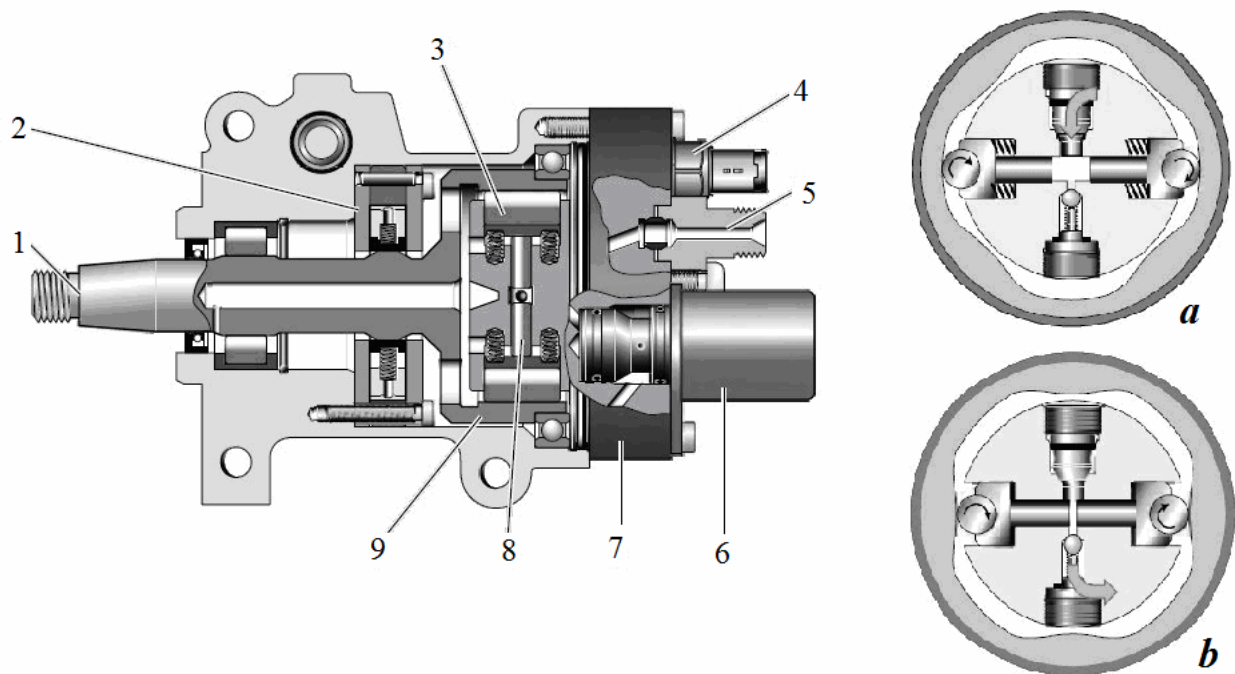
Pompa de injecție DFP 1: a- faza de admisie; b- faza de refulare: 1- ax antrenare; 2- pompa de transfer; 3- rolă; 4- senzor temperatură combustibil; 5- racord de înaltă presiune; 6- regulator de presiune; 7- cap hidraulic; 8- piston; 9- cilindru cu camă interioară (Sursa: Delphi)
